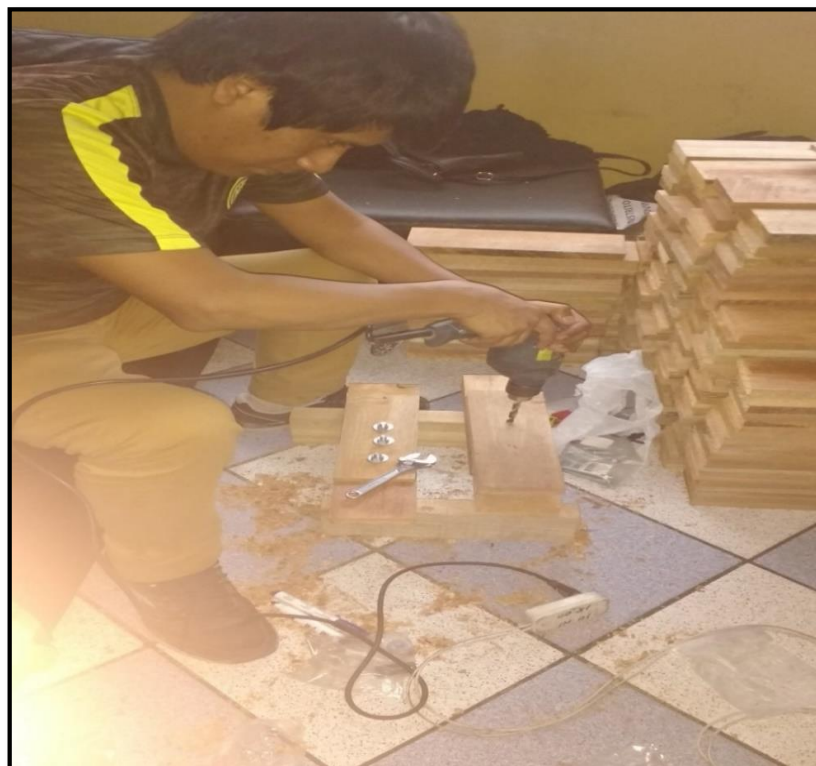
Empaquetado final de las piezas de madera.
